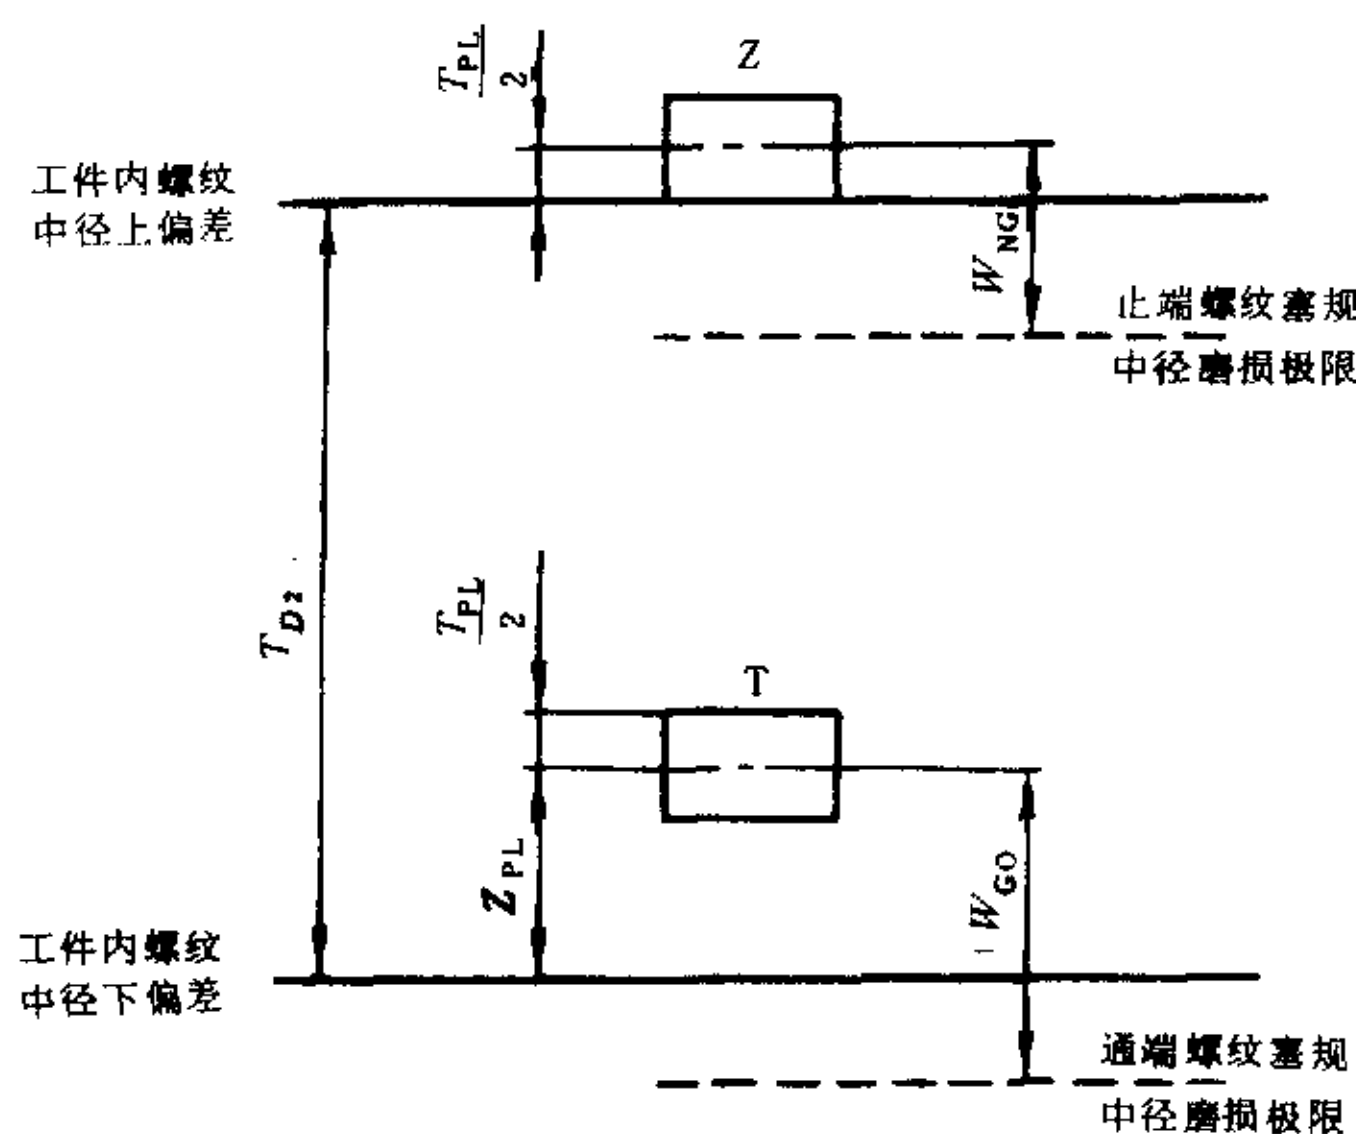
检查工件内螺纹用的螺纹塞规中径公差带图
